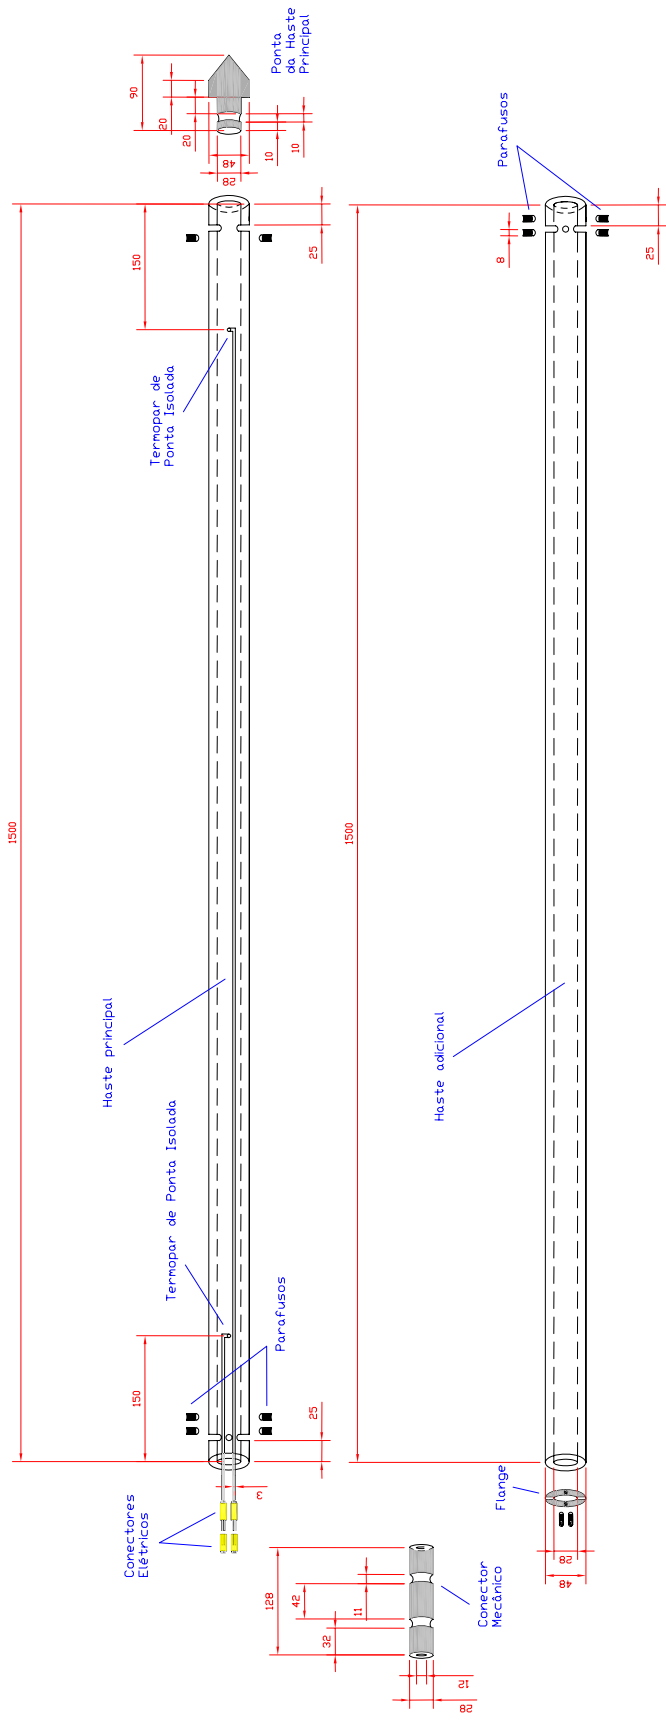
Esquema do projeto estrutural do conjunto sonda-termopares-haste (dimensões em milímetros)
